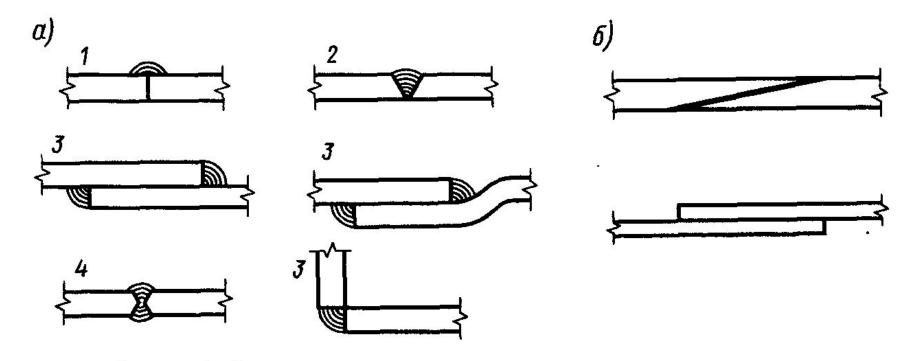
Сварные соединения термопластических пластмасс:
